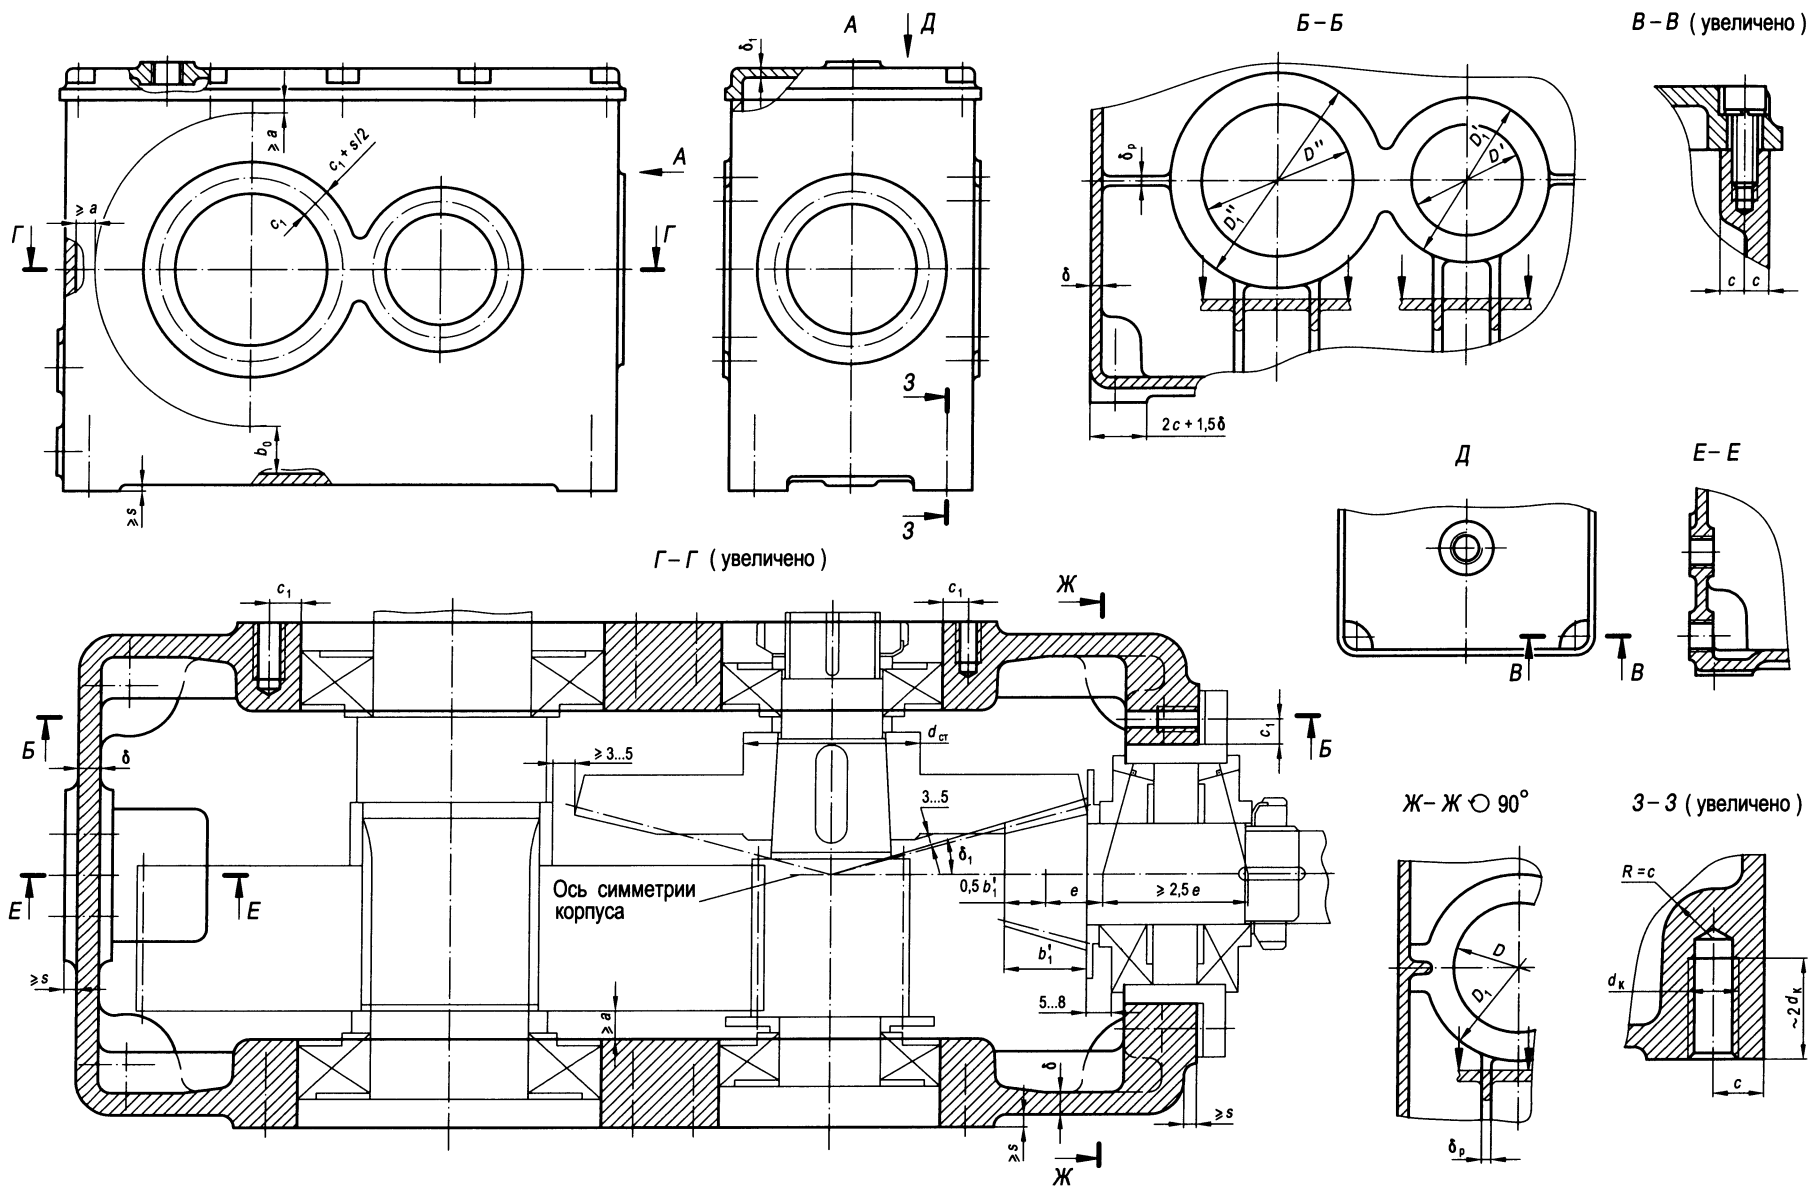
Определение размеров корпуса коническо-цилиндрического редуктора типа 5 (см. рис. 23.2.1, д; размеры см. на листах 23.2; 23.3)
